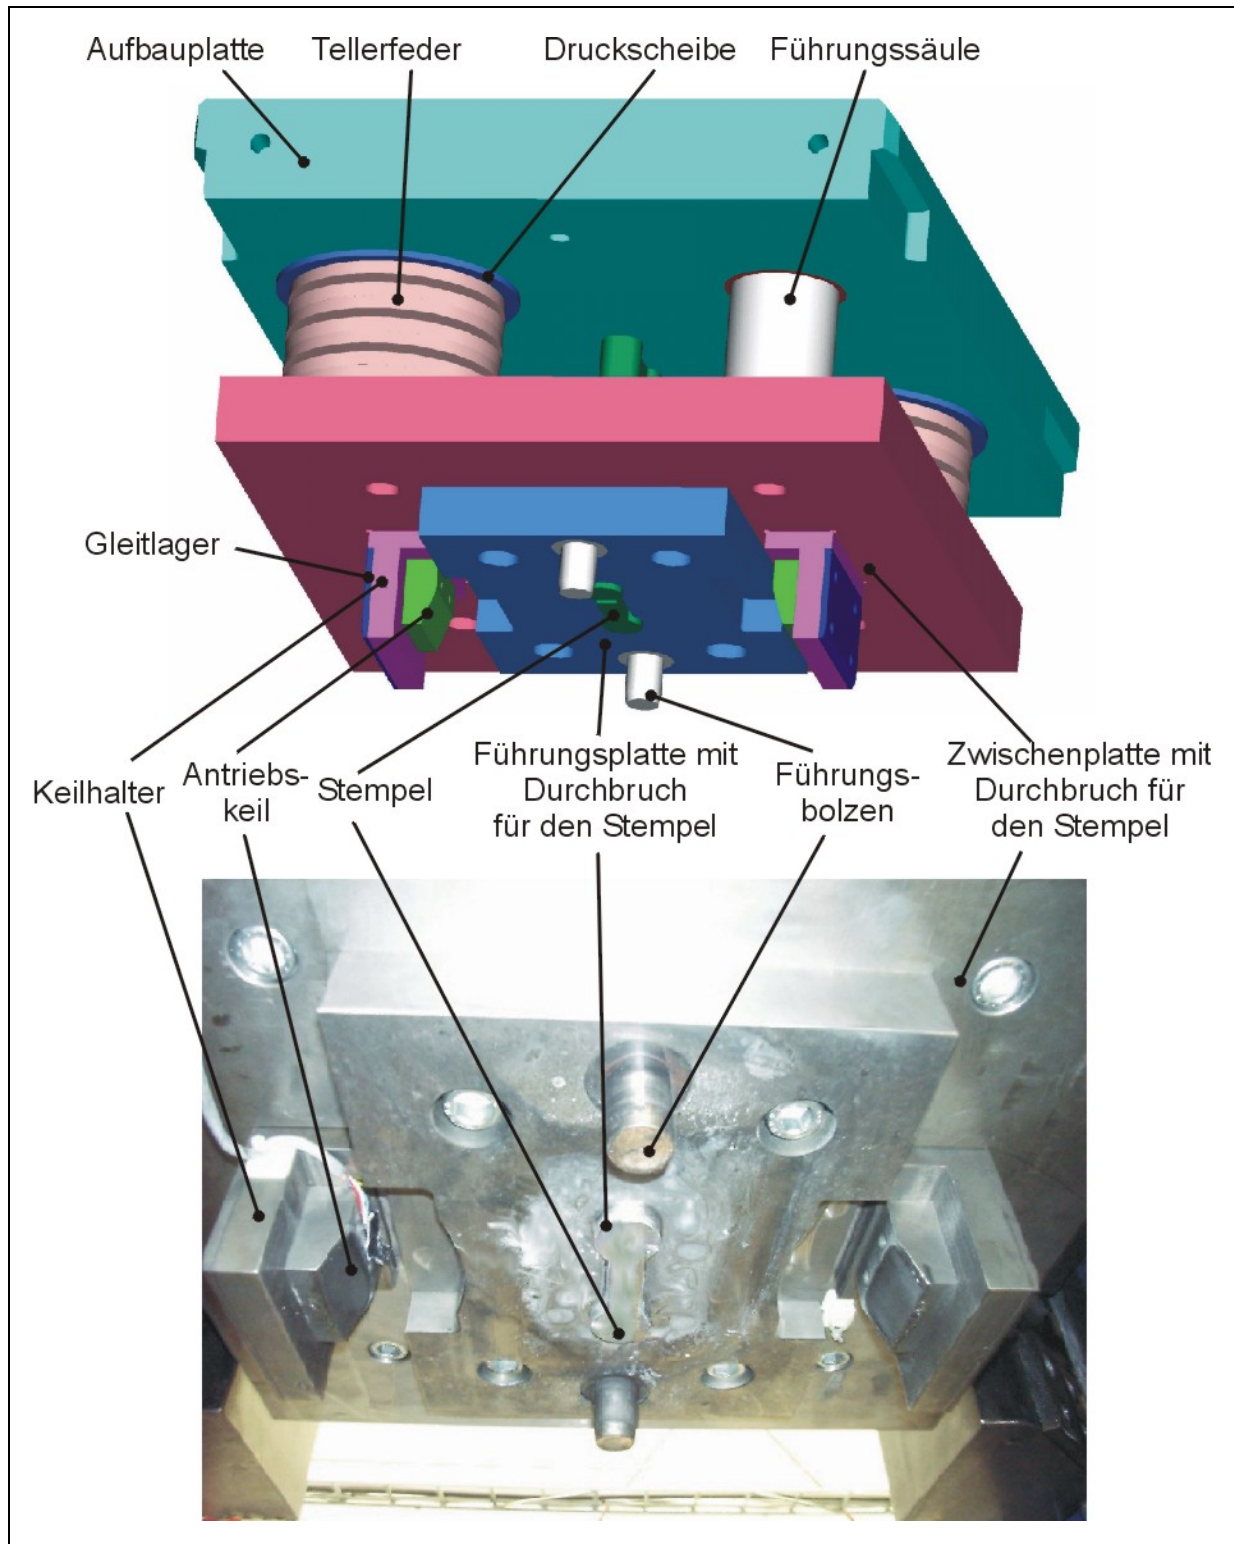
zeigt den Aufbau des Oberwerkzeugs. Auf der Aufbauplatte ist der Stempel kraftschlüssig befestigt. Die Befestigung der Keile erfolgt kraftschlüssig auf einer Zwischenplatte, die wiederum über vier Säulen geführt und auf insgesamt vier Federpaketen, die jeweils aus sieben wechselsinnig angeordneten Tellerfedern bestehen, gelagert ist. Aufgabe des Federpaketes ist es, die zeitliche Entkopplung der horizontalen von der vertikalen Umformung zu ermöglichen sowie die erforderlichen Kräfte für die horizontale Umformung bereitzustellen. Darüber hinaus müssen sie die erforderliche Schließkraft der Schieber während der vertikalen Umformung erzeugen, um eine Öffnung der Werkzeugelemente zu verhindern.
